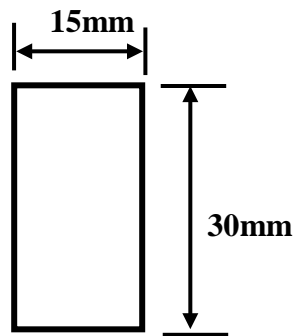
Pemasangan spesimen uji tekan Universal Tesile Machine type UTM-C05T
